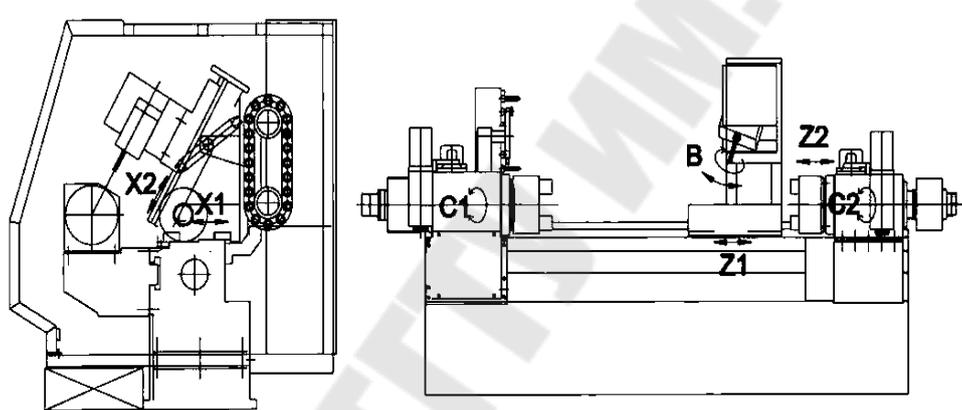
Центр токарный мод. САТ630 с токарно-фрезерной головкой (осью В), инструментальным магазином с устройством автоматической смены инструмента, протившпинделем, устройствами позиционирования и круговой подачи шпинделя (осью С1) и протившпинделя (осью С2)
